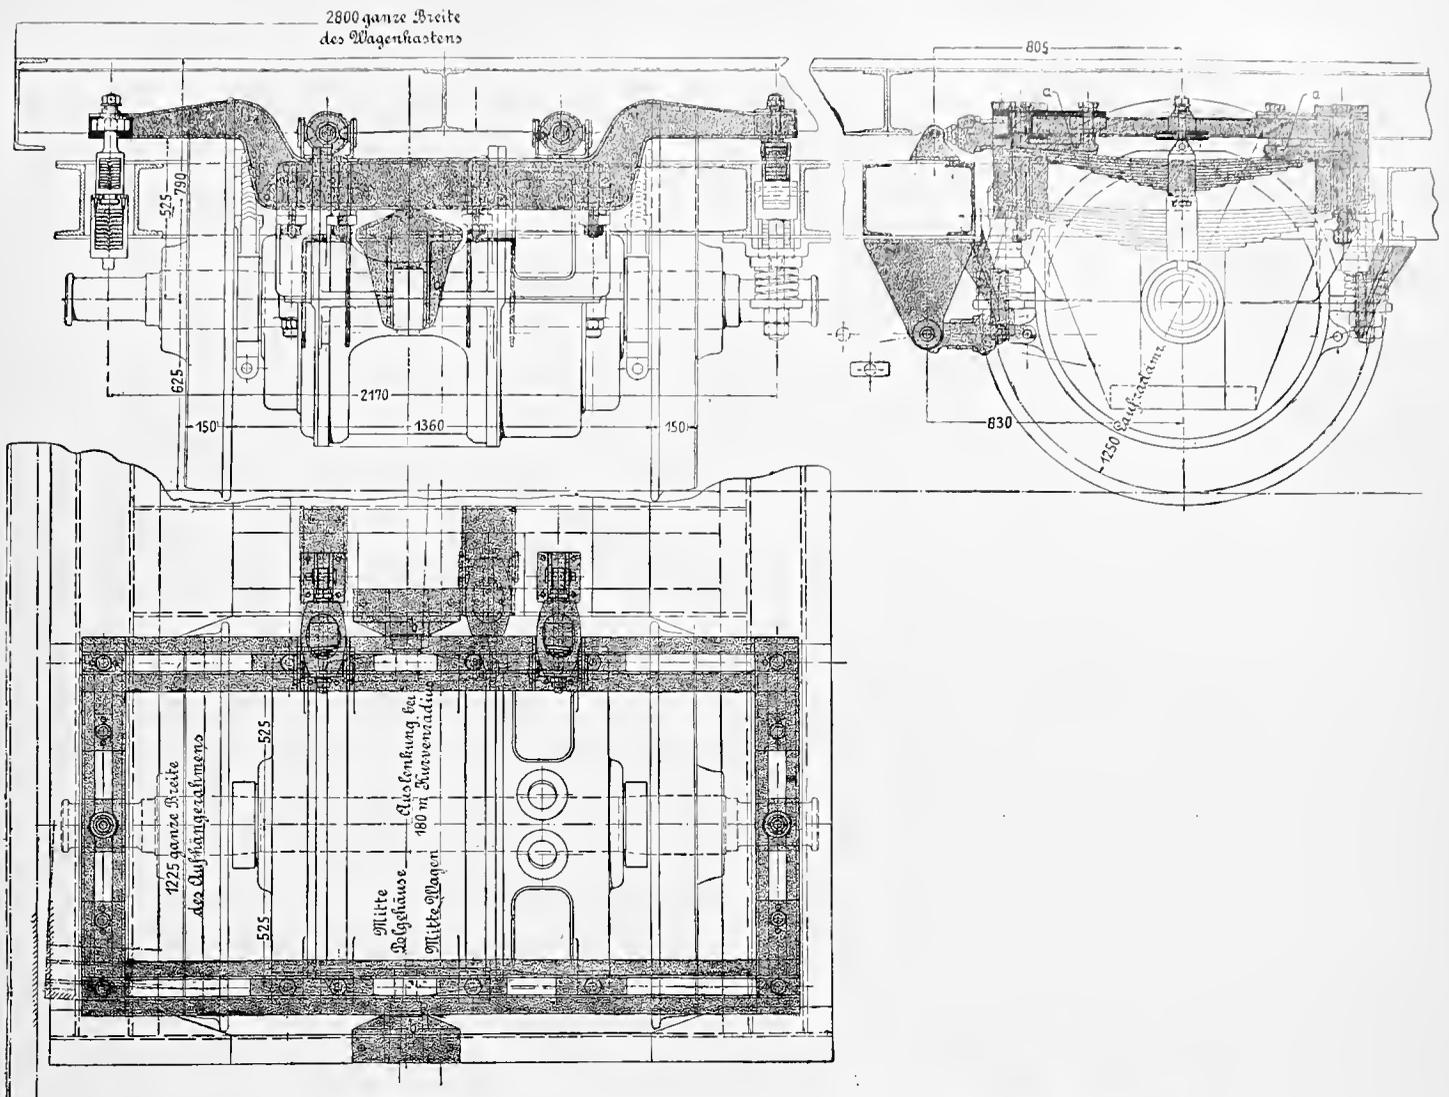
Motor in besonderem Rahmen mit kleiner kräftiger Abfederung.
